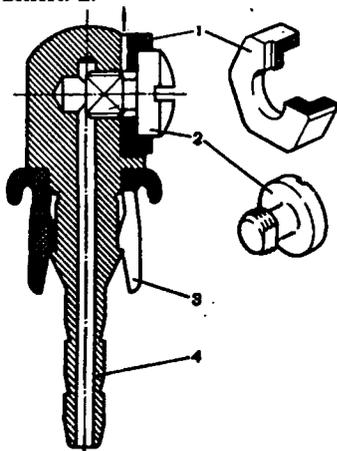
Жиклер омывателя ветрового стекла: 1 - распылитель; 2 - винт; 3 - втулка; 4 - корпус жиклера со штуцером
